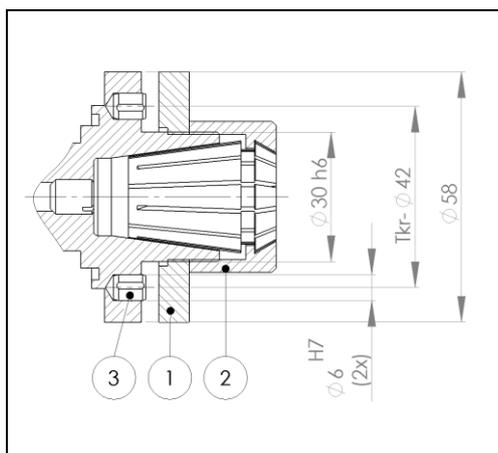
Werkzeugaufnahme ATLOCK Spannflansch
